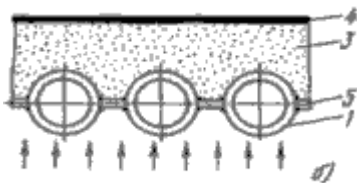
б. Топочный гладкотрубный экран с сварными проставками (мембранный): 1 - труба; 3 - тепловая изоляция; 4 - уплотнительный слой (обмазка, металлический лист); 5 - металлическая проставка;
